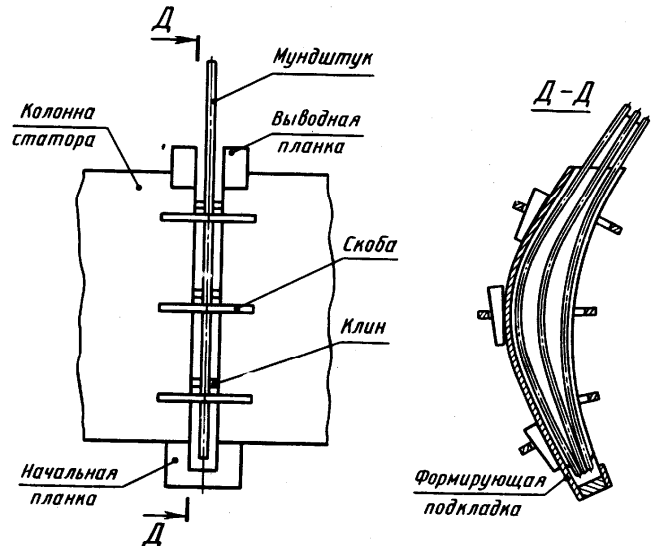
Схема сборки под сварку колонны статора гидротурбины
